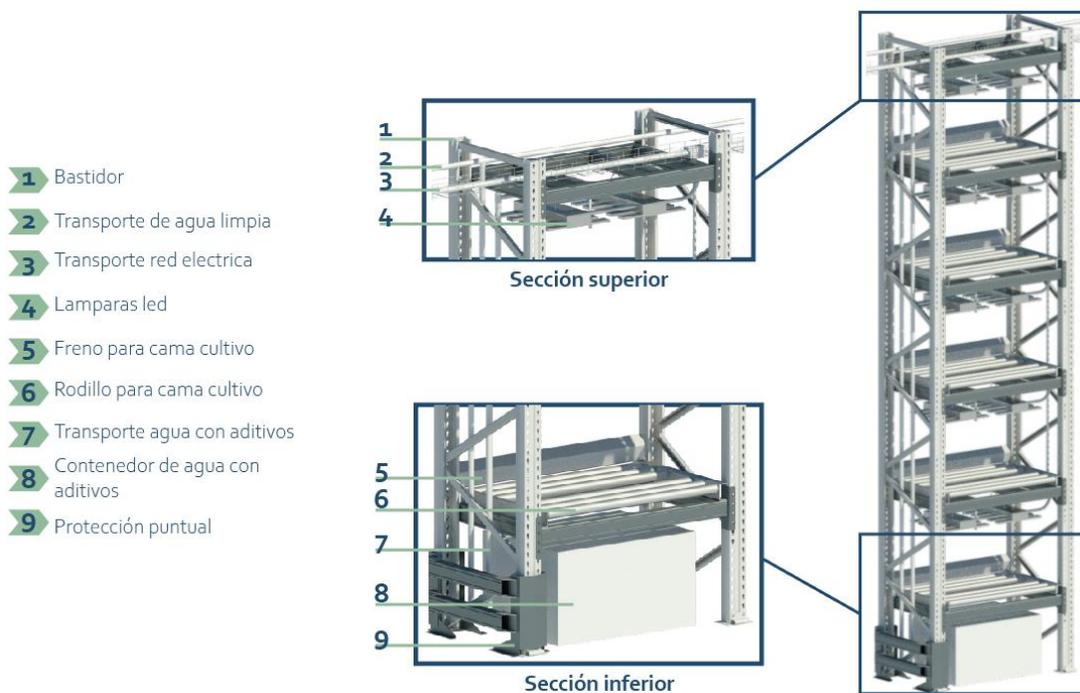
Detalle estructura vertical cama cultivo (ver anexo “Detalles cama cultivo”)
